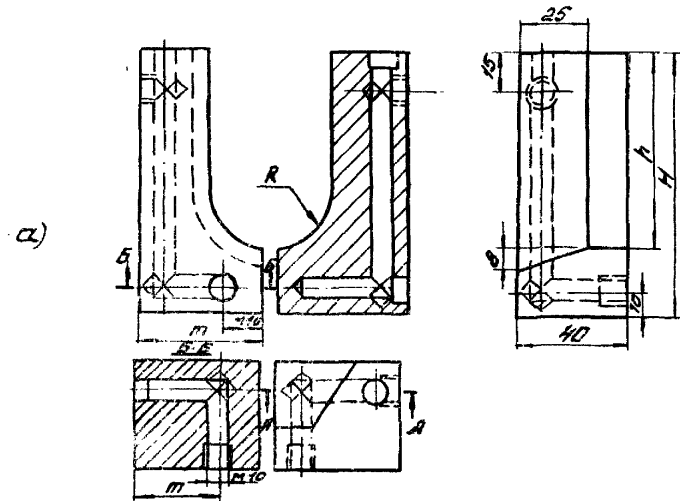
Рабочие чертежи медных форм для сварки втавр спаренных стержней.
